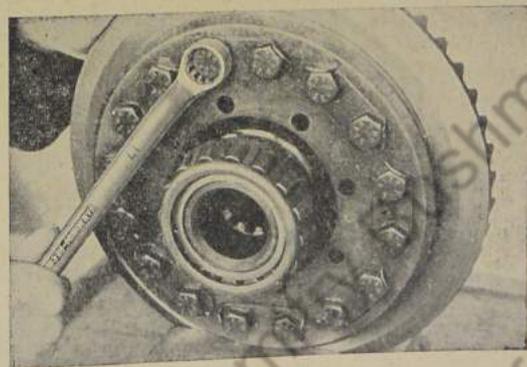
Tellerrad vom Ausgleichgetriebe abschrauben
